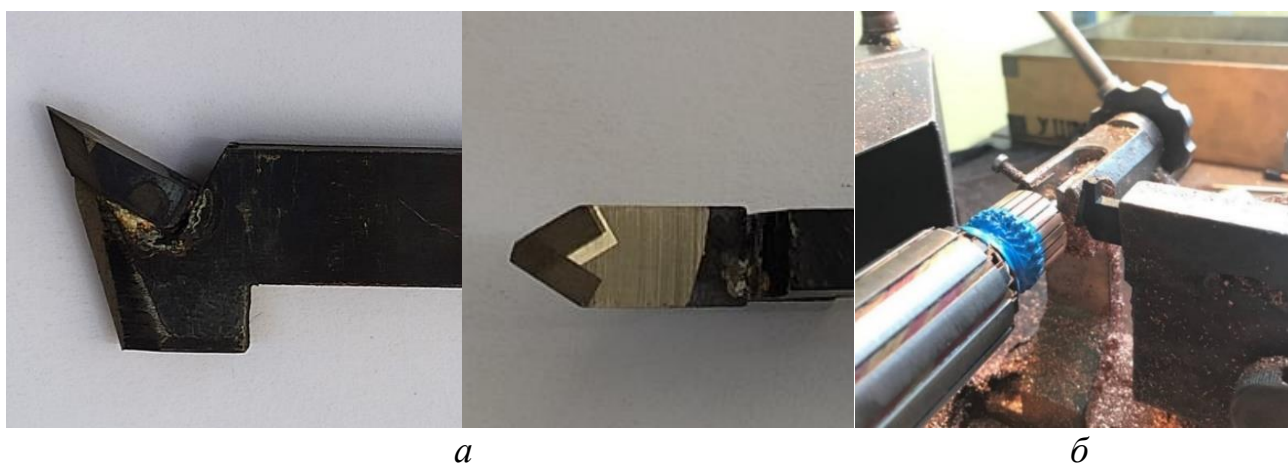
Резец с напаянной твёрдосплавной пластиной: а – пластина ВК8 специальной геометрии; б – процесс обработки коллектора ротора
